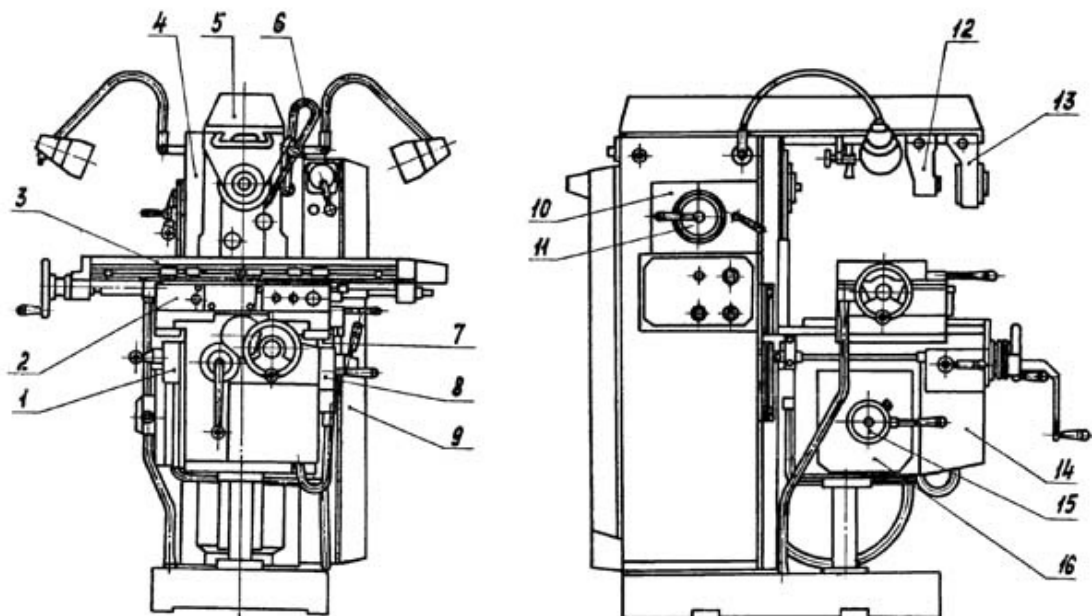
Розташування складових частин фрезерного верстата 6P80
